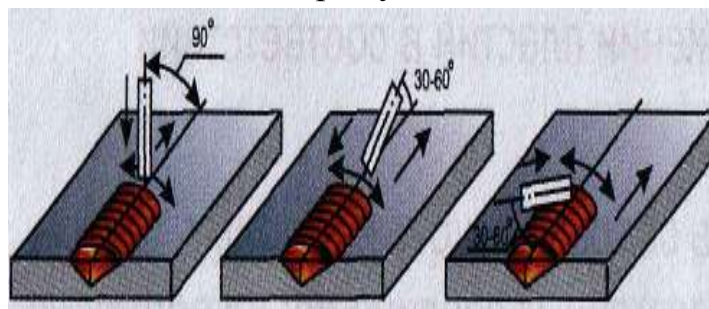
Движения электрода при сварке стыковых соединений с разделкой кромок.
